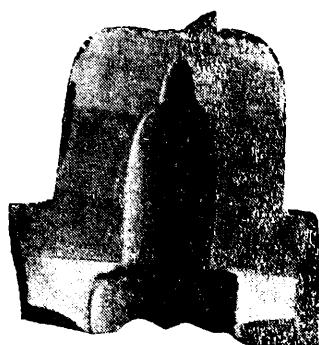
Разрез отливки торцевой фрезы с утепленной прибылью
